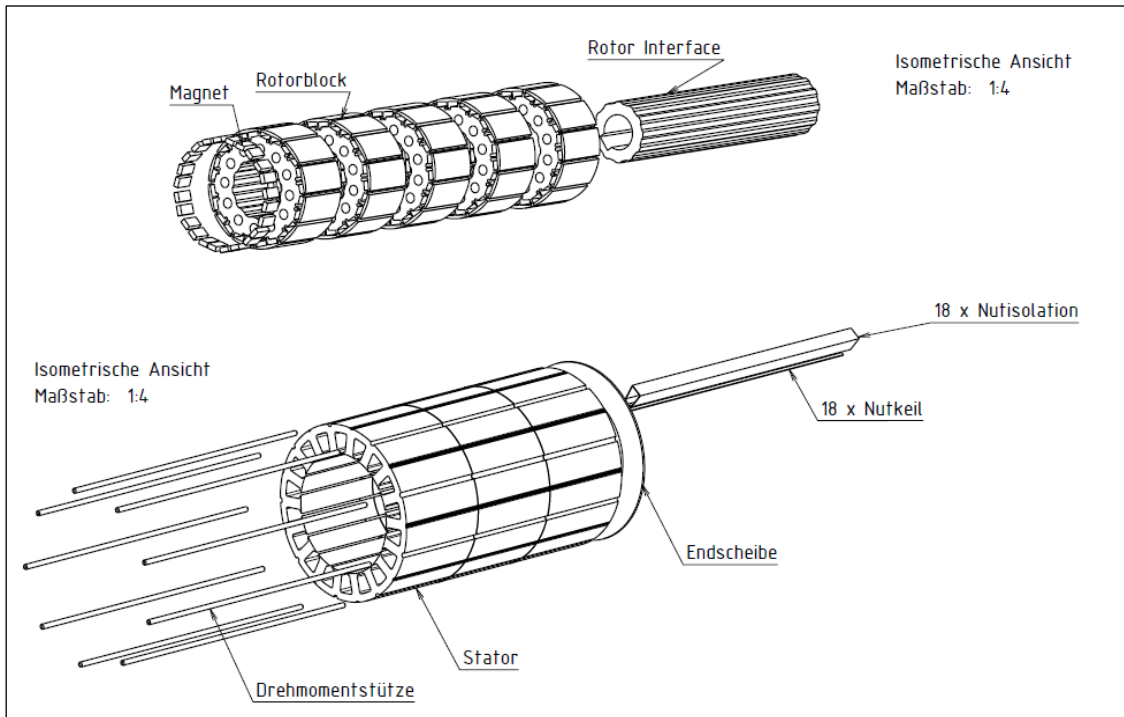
Zusammenbau der Baugruppe Motor M1
